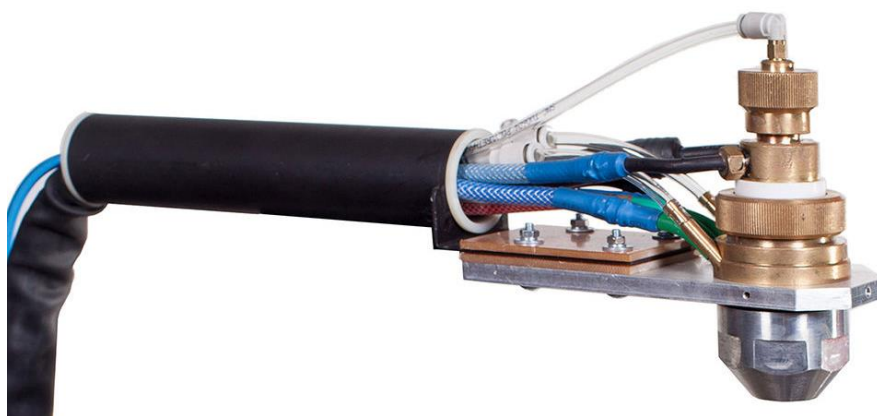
Плазматрон для автоматической плазменной наплавки ПМН-2
